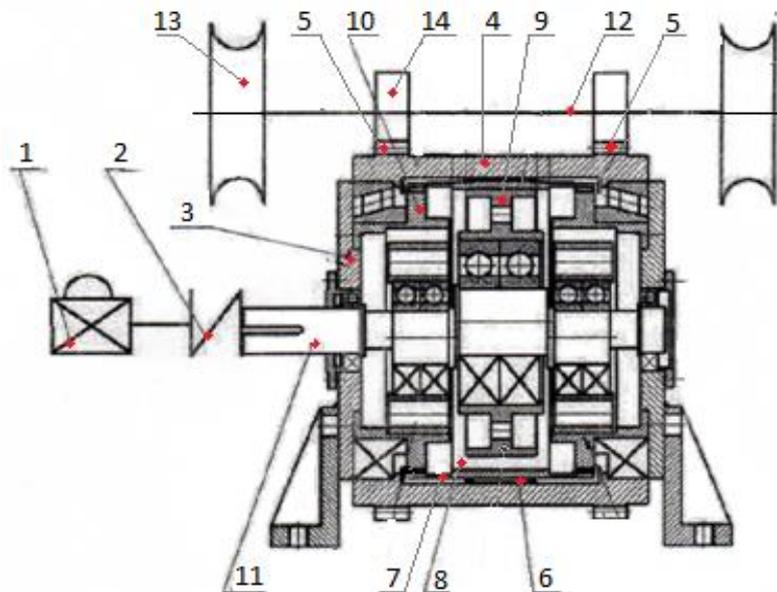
Конструктивная схема привода передвижения металлургической машины
